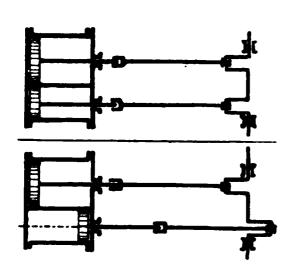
Woolfsche Maschine mit gleichgerichtetem Kolbenlauf. Bei den Woolfschen Maschinen arbeitet der Niederdruckcylinder stets ohne Expansion.
